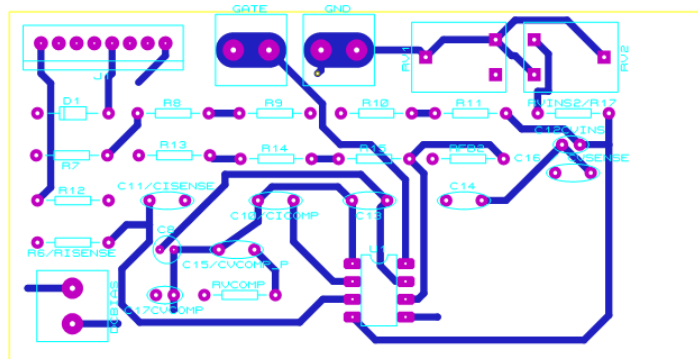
Cara posterior del PCB del circuito de control, prototipo final.
